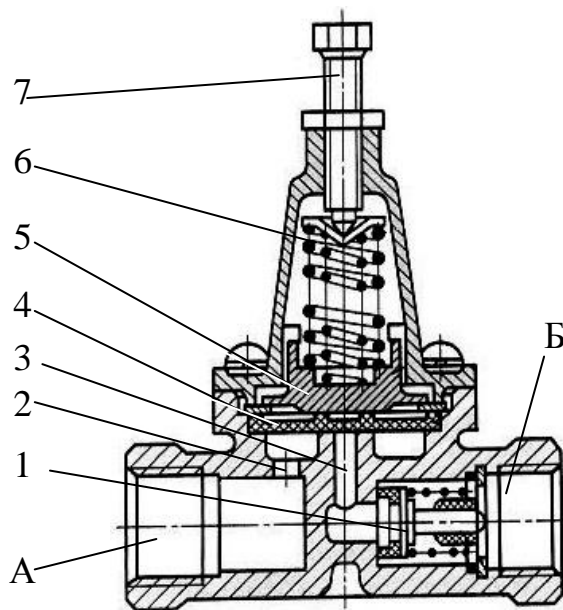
Конструкция одинарного защитного клапана грузового автомобиля-тягача КАМАЗ: 1 – обратный клапан; 2 и 3 – каналы; 4 – мембрана; 5 – поршень; 6 – пружина; 7 – регулировочный винт; А – вывод к перепускному клапану контура № 3; Б – вывод в питающую линию прицепа
